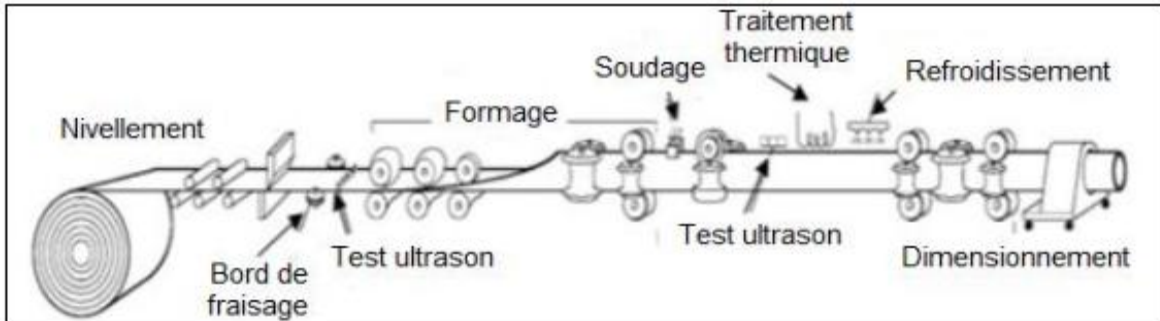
Technique de fabrication des tubes soudés en spirale [2]
